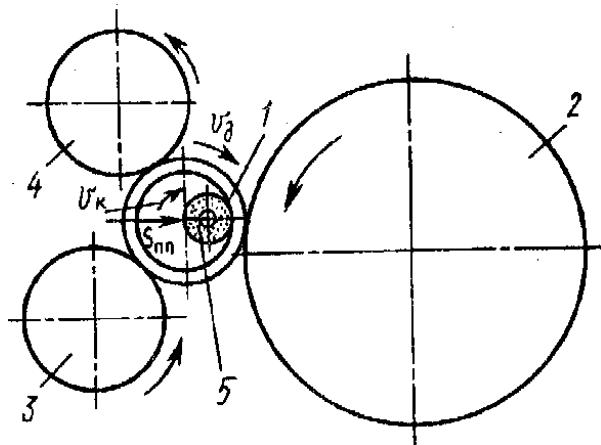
Схема внутрішнього безцентрового шліфування [24]
